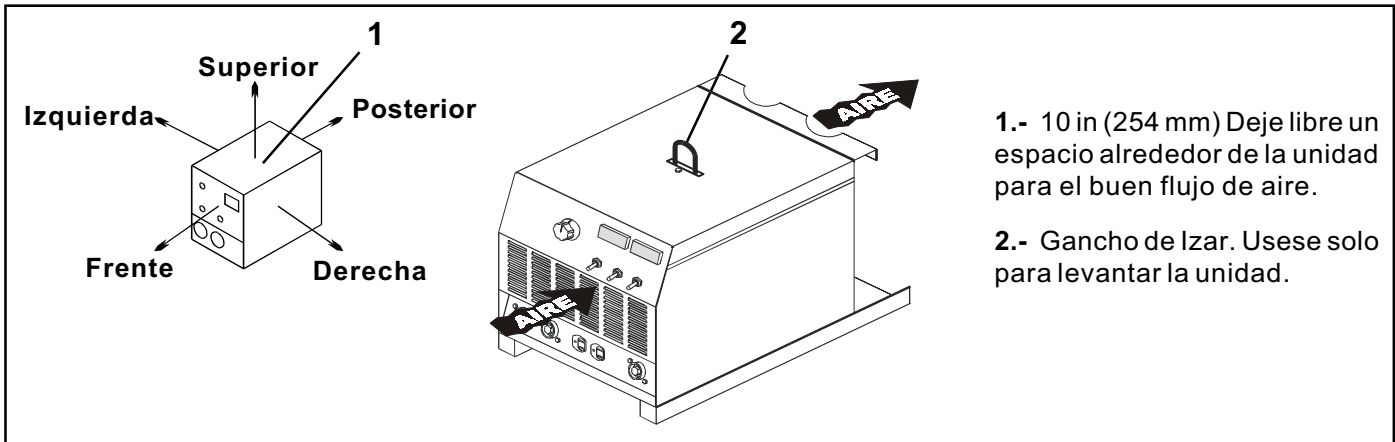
Localización y Movimiento de la Máquina Soldadora.
